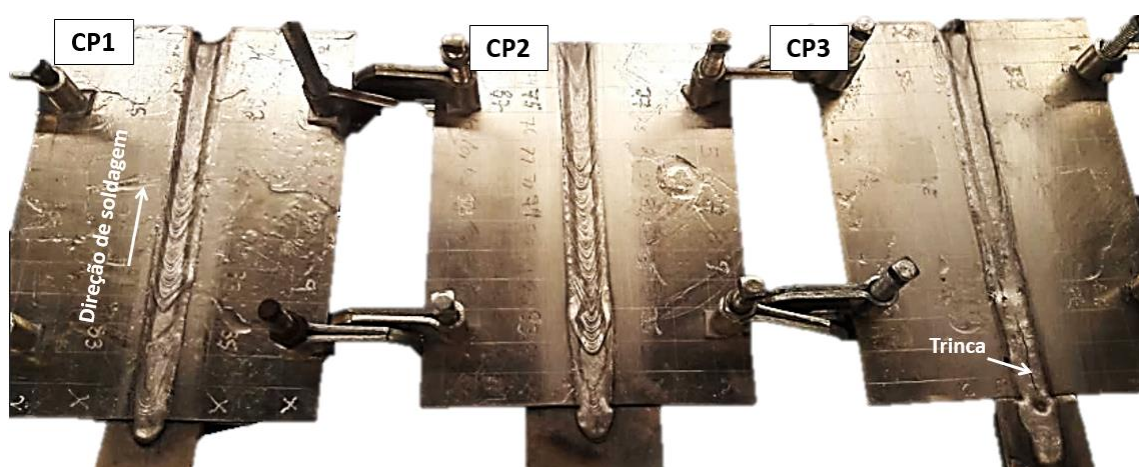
Corpo de prova 01, 02 e 03 soldados com processo GMAW.
